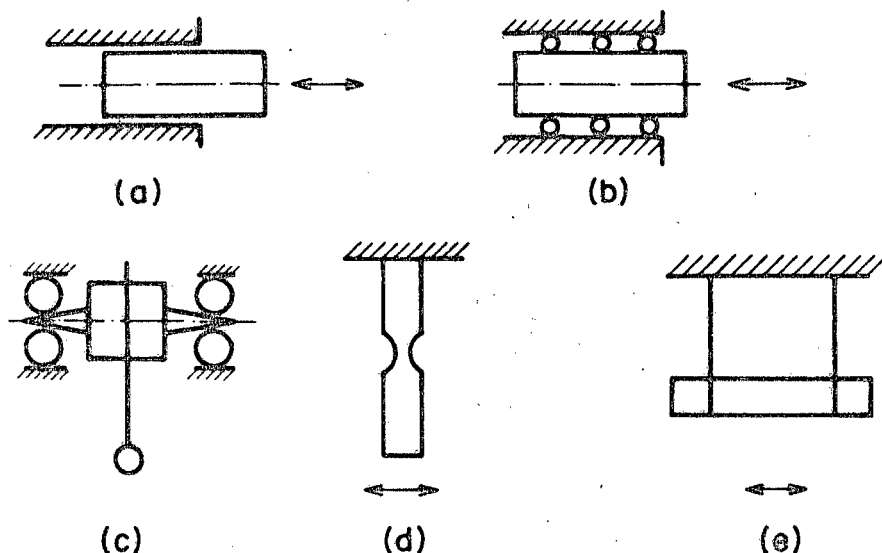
a) bucha deslizante; b) guia axial com esferas;
